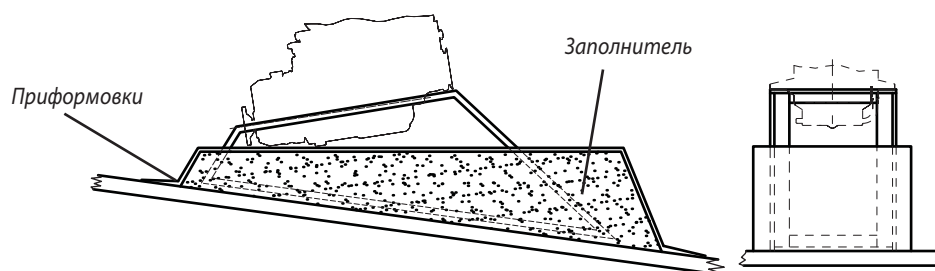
Легкий стальной фундамент для бензинового двигателя
